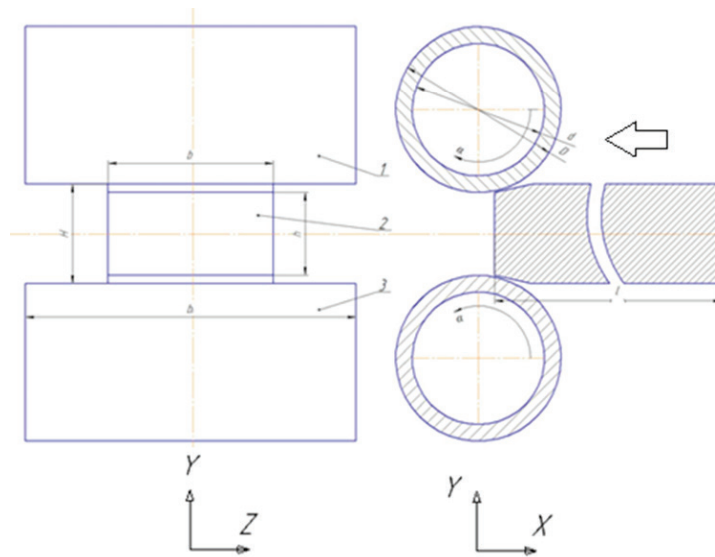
Расчетная схема: 1, 3 — валки; 2 — заготовка
